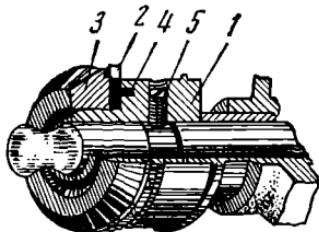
Зубчатый барабан в кинопроекторе ПП-16-4: 1 — корпус; 2 — зубчатый венец; 3 — реборда; 4 — штифт; 5 — винт крепления
